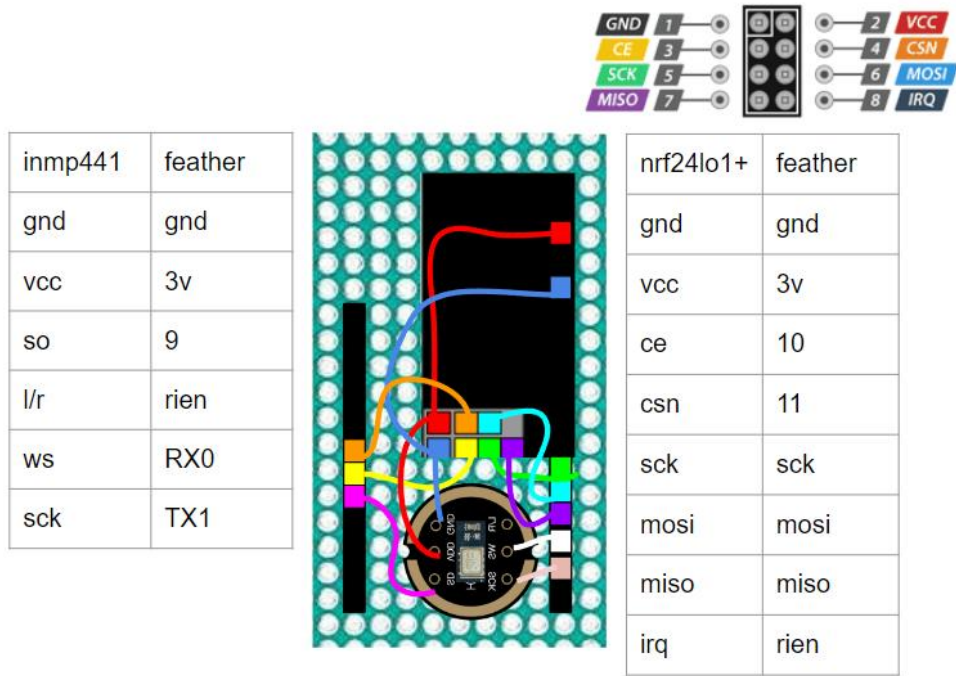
lien et soudage sur la protoboard de la partie micro
